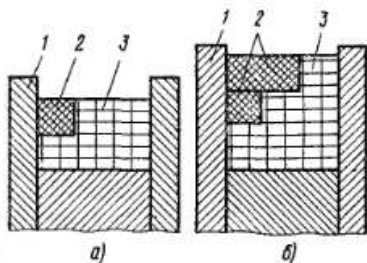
Установка закладных колец для намотки ступенчатых катушек
